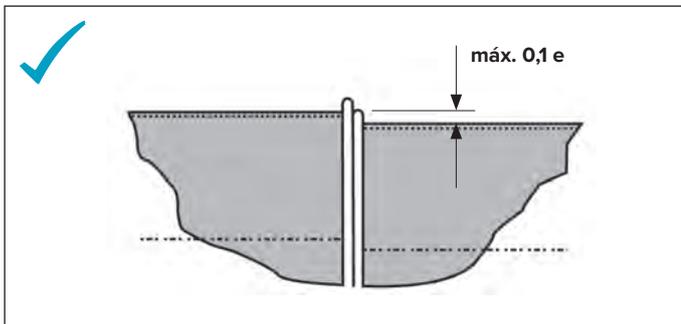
Cordón de soldadura con desajuste (satisfactorio)
